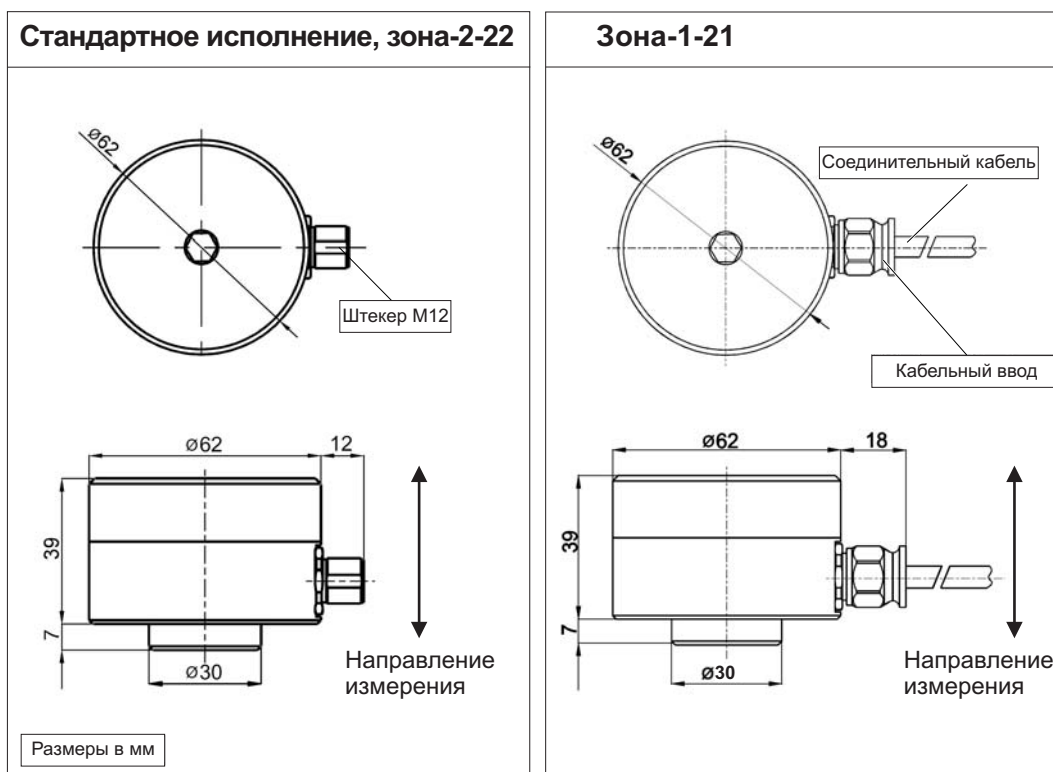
Размеры корпуса и направление измерения: стандартное исполнение, зона-2-22.
